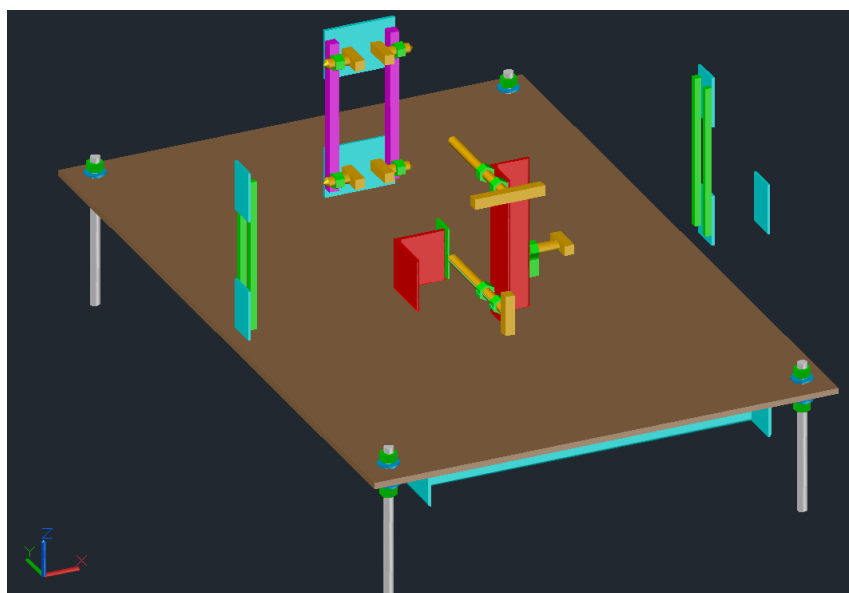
Preparo da Peça de teste para o procedimento de soldagem na posição 2G
